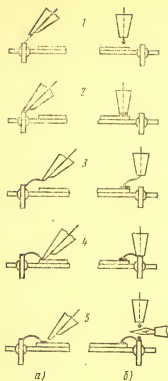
Образование проволочных перемычек при термокомпрессионной сварке капиллярным инструментом:
